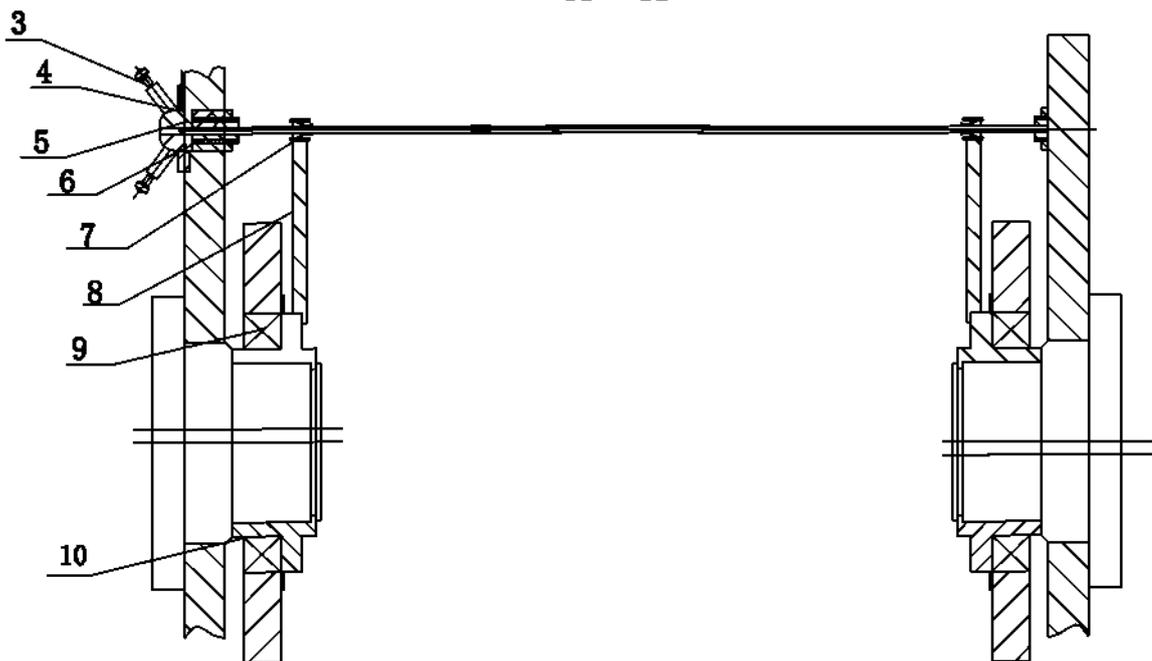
Регулировка зазора между верхней ножевой балкой и кромкой ножа
